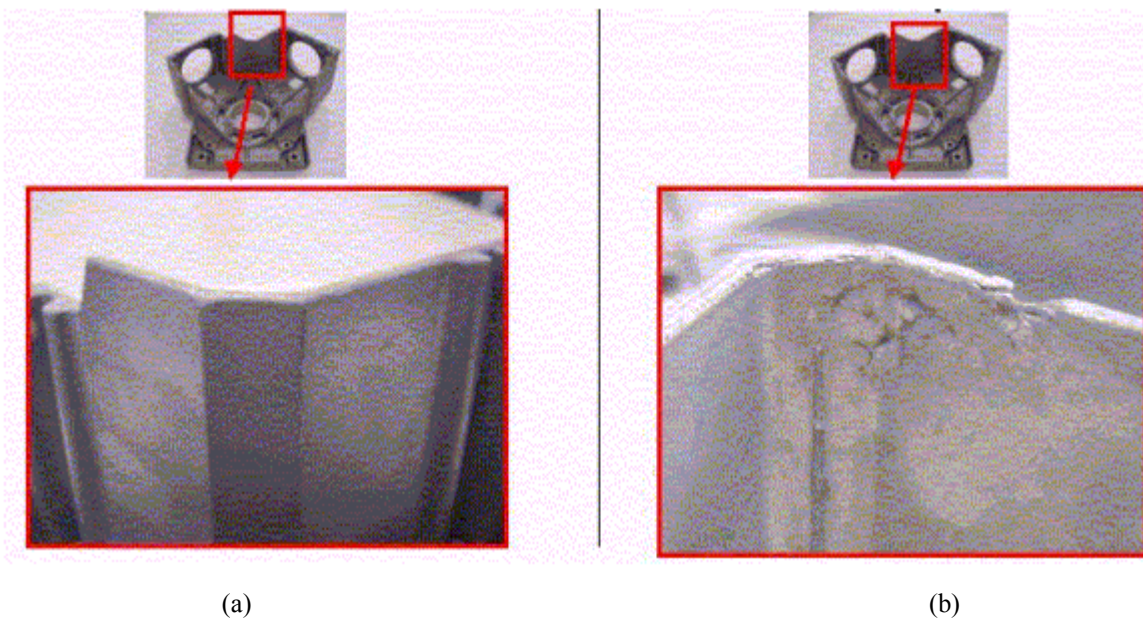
Peça sem solda fria (a) e peça com solda fria (b).
